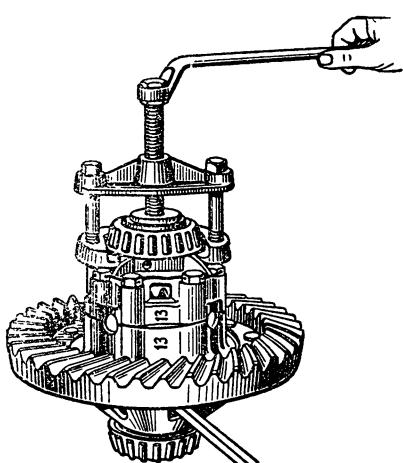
Спрессовка съемником внутреннего кольца с подшипника с роликами с шейки корпуса
